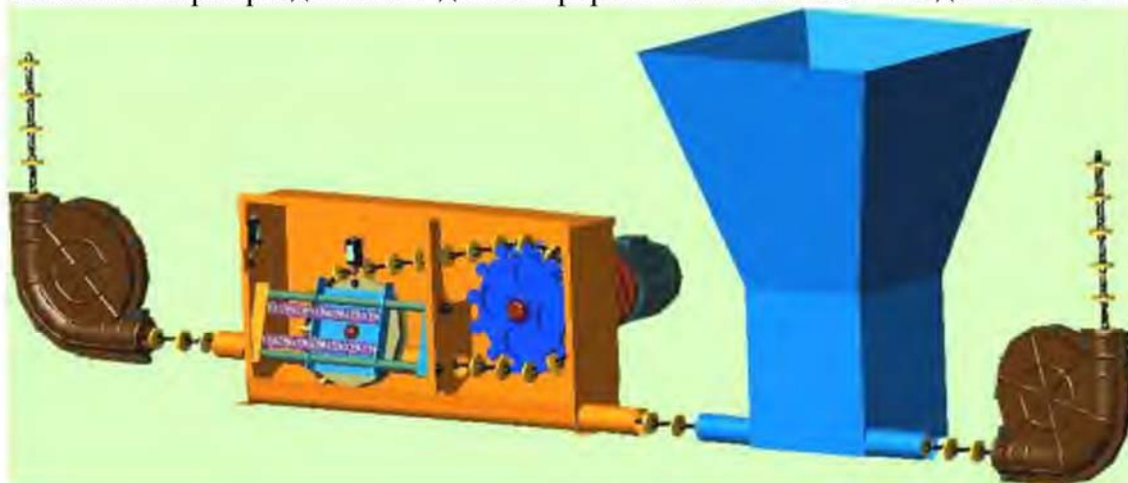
Конструктивный вид канатного транспортеры для раздачи корма
